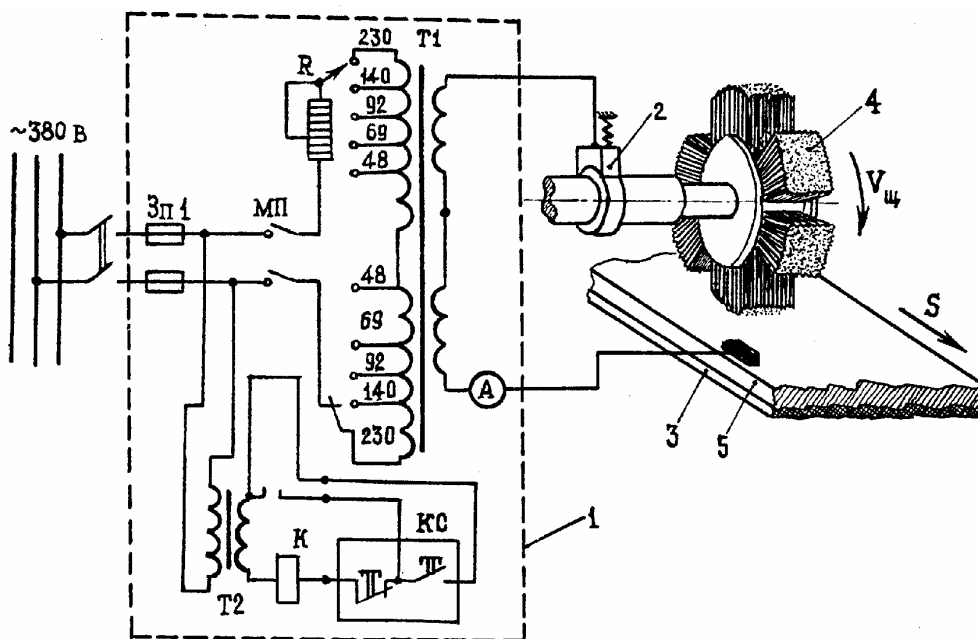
Установка для поверхневого оброблення листового прокату, змонтована на базі металорізального верстату.
